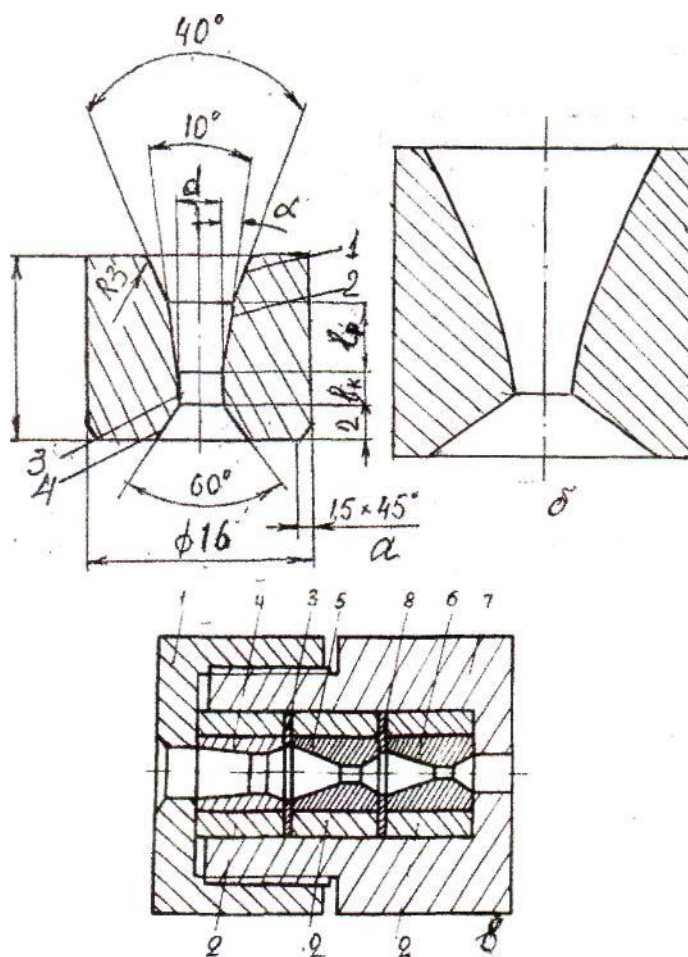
Проектний профіль форми 9 волоки (а) (1 - мастильний конус; 2 - робочий конус; 3 - калібрувальний пояс; 4 - вихідна распушка); фактичний профіль волоки (б): збірна волока (1-кришка-гайка; 2 - обойма; 3,8 - шайби; 4 - напірна волока; 5, 6-робочі волоки; 7 - корпус).
